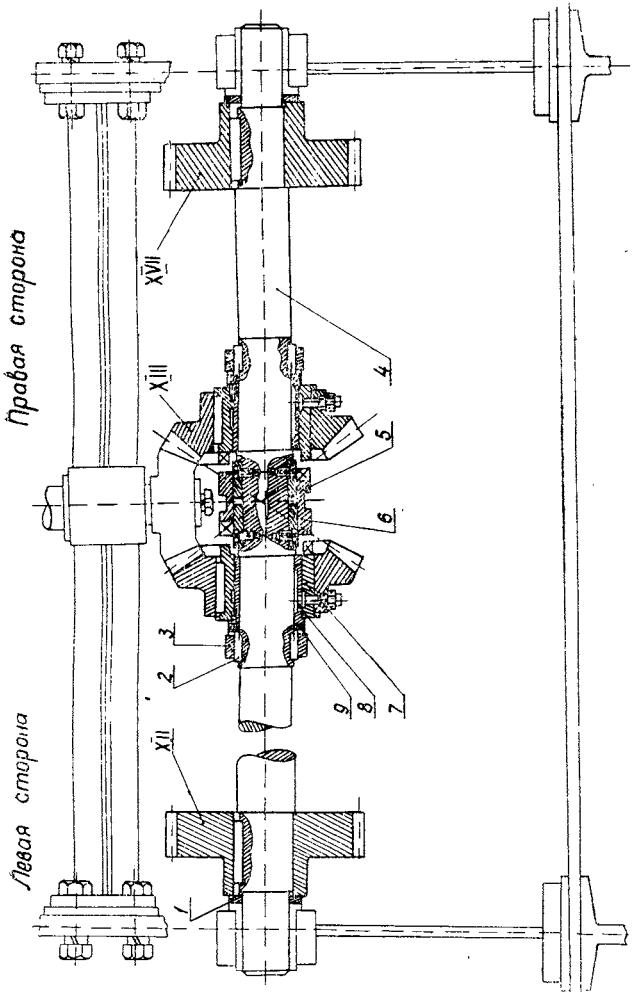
Горизонтальный вал механизма подъема стрелы.
